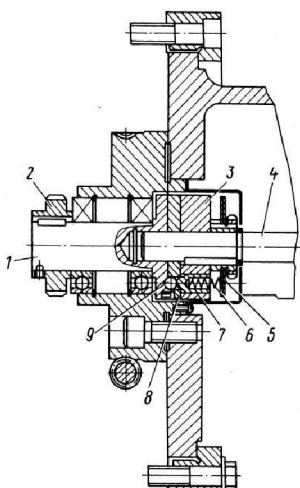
Рукав: 1, 3 – полумуфты; 2 – зубчатое колесо; 4 – вал; 5 – шайба; 6 – пружина; 7 – толкатель; 8 – сепаратор; 9 – шарик
